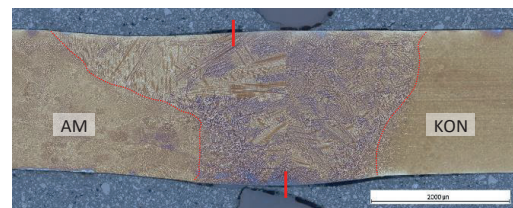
Wurzelversatz beim WIG-Schweißen einer hybriden Nickelbasislegierung: links DED-LB(w), rechts konventioneller Grundwerkstoff, Inconel 718.
